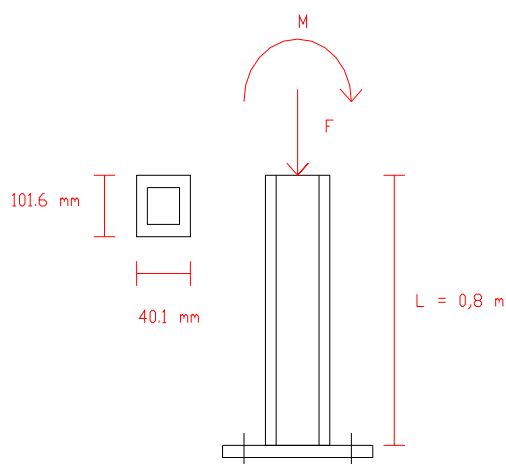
COLUMNA DE SOPORTE PARA LA MARMITA
